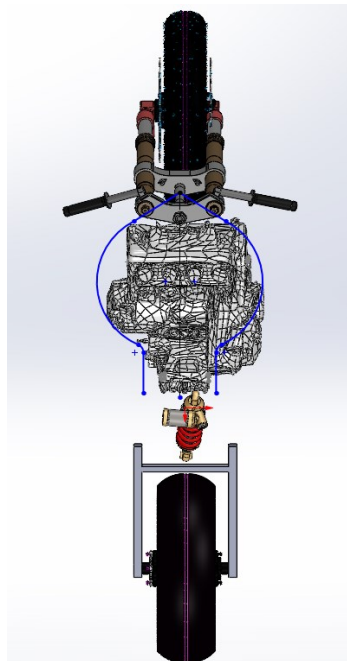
Vista de planta de la posición del chasis sobre el conjunto.
